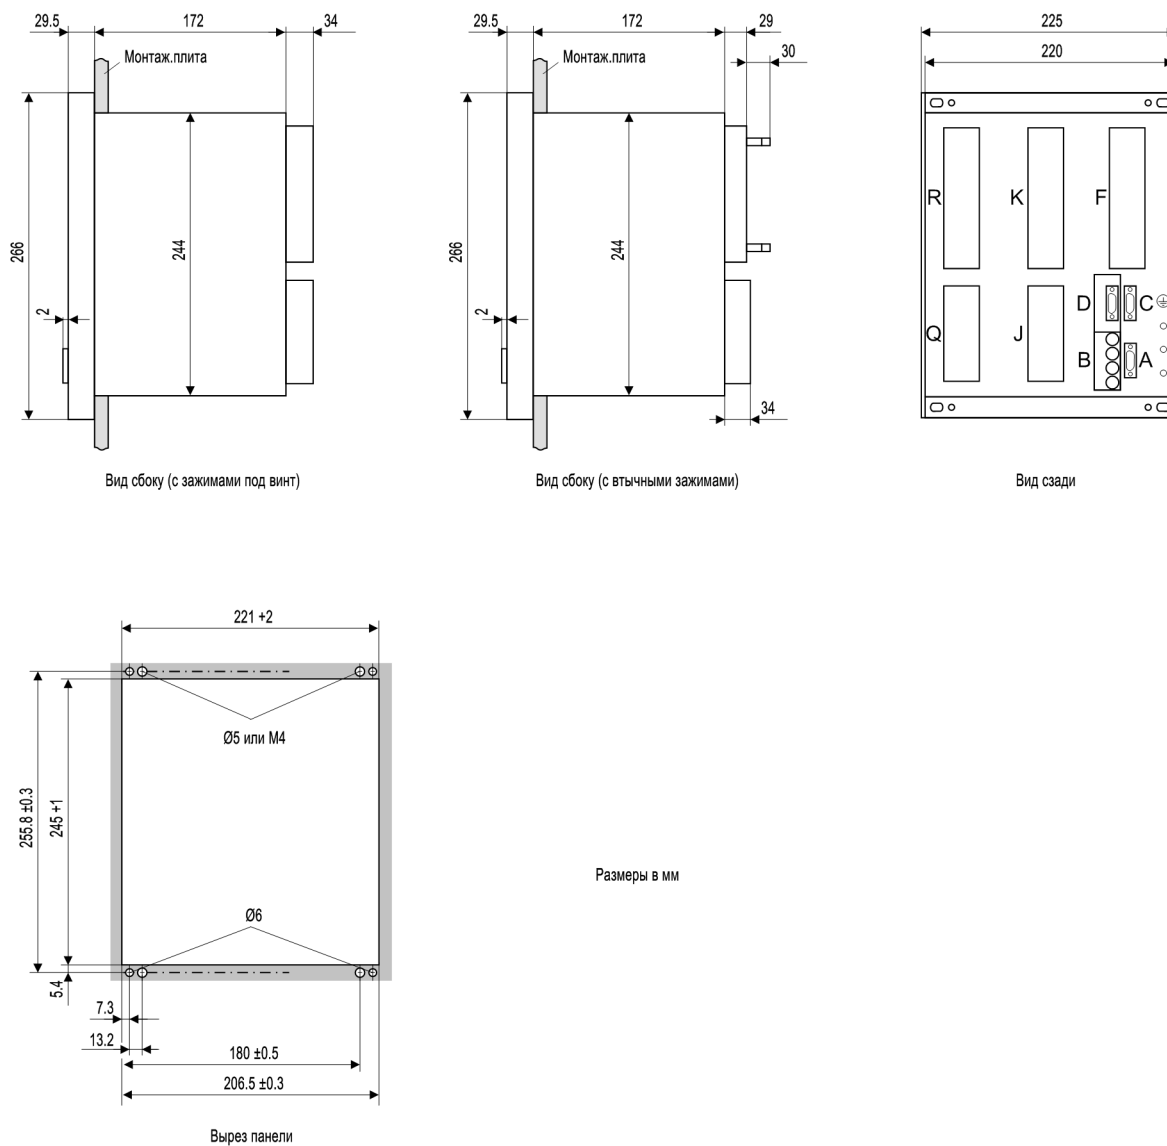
Размерные эскизы вариантов устройства 7UM621 или 7UM623 для встраиваемого монтажа устройства в шкаф / панель (размер корпуса 1/2)
